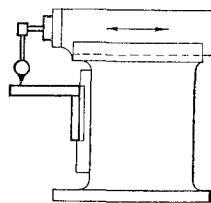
Проверка перпендикулярности направляющих салазок к направляющим станины токарного станка.
